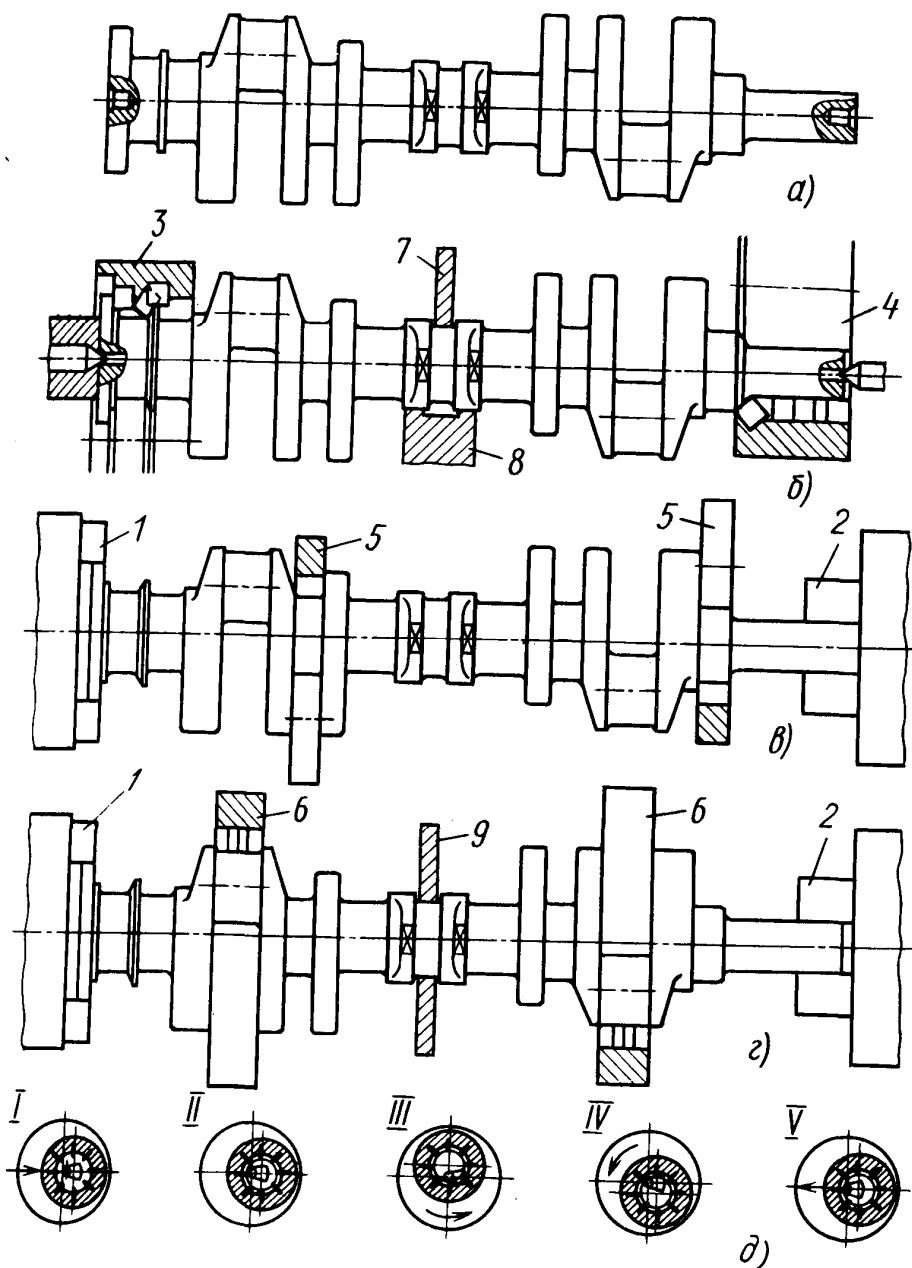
Схеми контурного фрезерування заготовки колінчастого вала: а – заготовка; б – фрезерування хвостовиків та фланця; в – фрезерування корінних шийок; г – фрезерування шатунних шийок; д – положення, які займає фреза в процесі обробки
